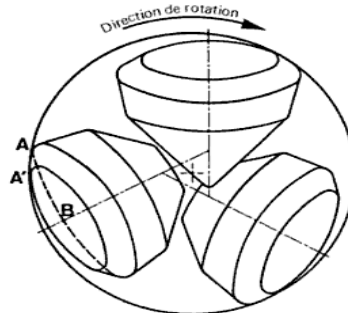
Vue de dessus des molettes d'un outil. [10]
